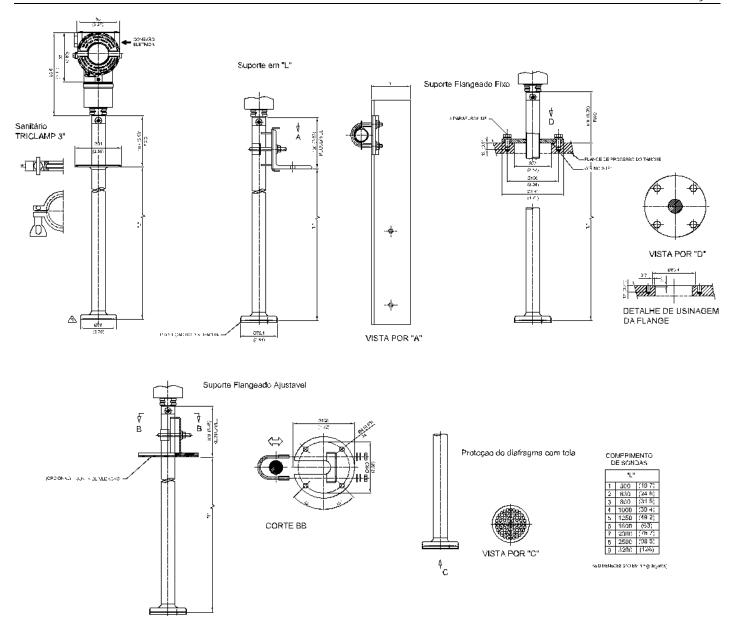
(d)- Desenho Dimensional de Montagem do LD292 – Nível (Inserção)
